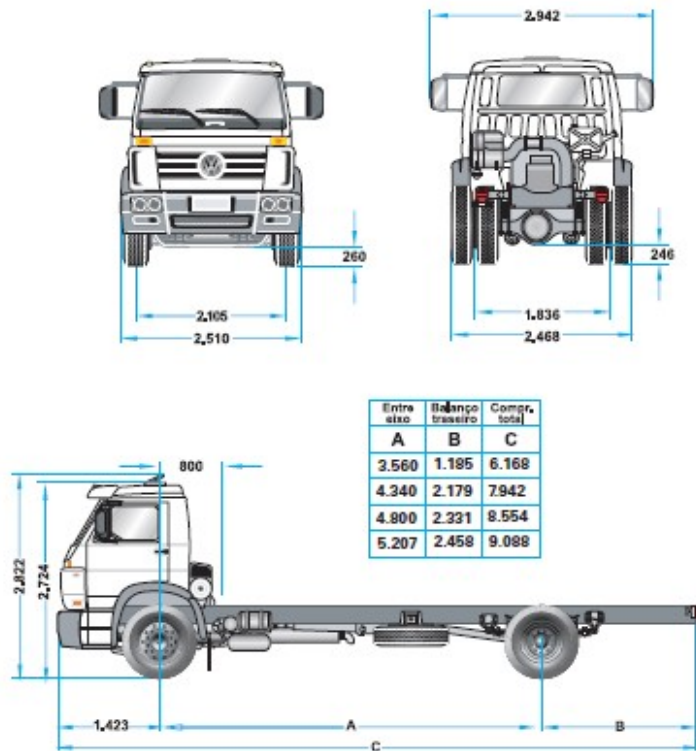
Dimensões Principais (mm) WV Worker 15-180
